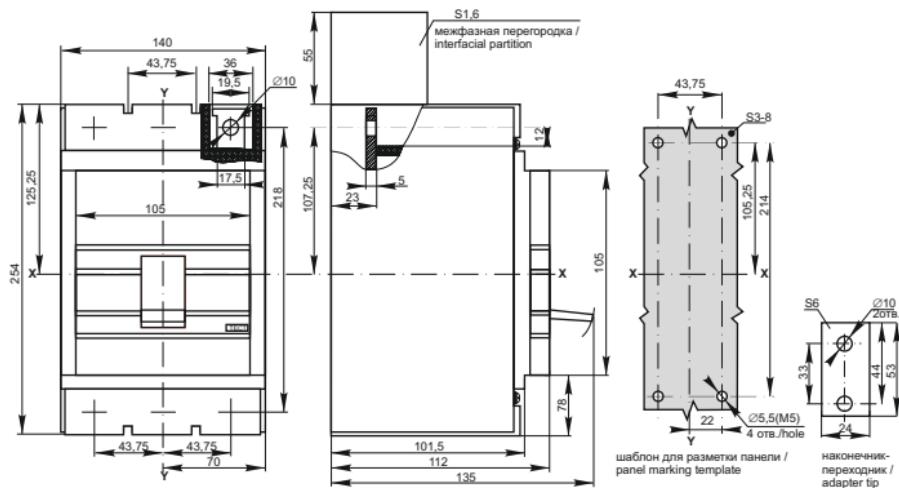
Габаритные и установочные размеры выключателя BA88-37 /
